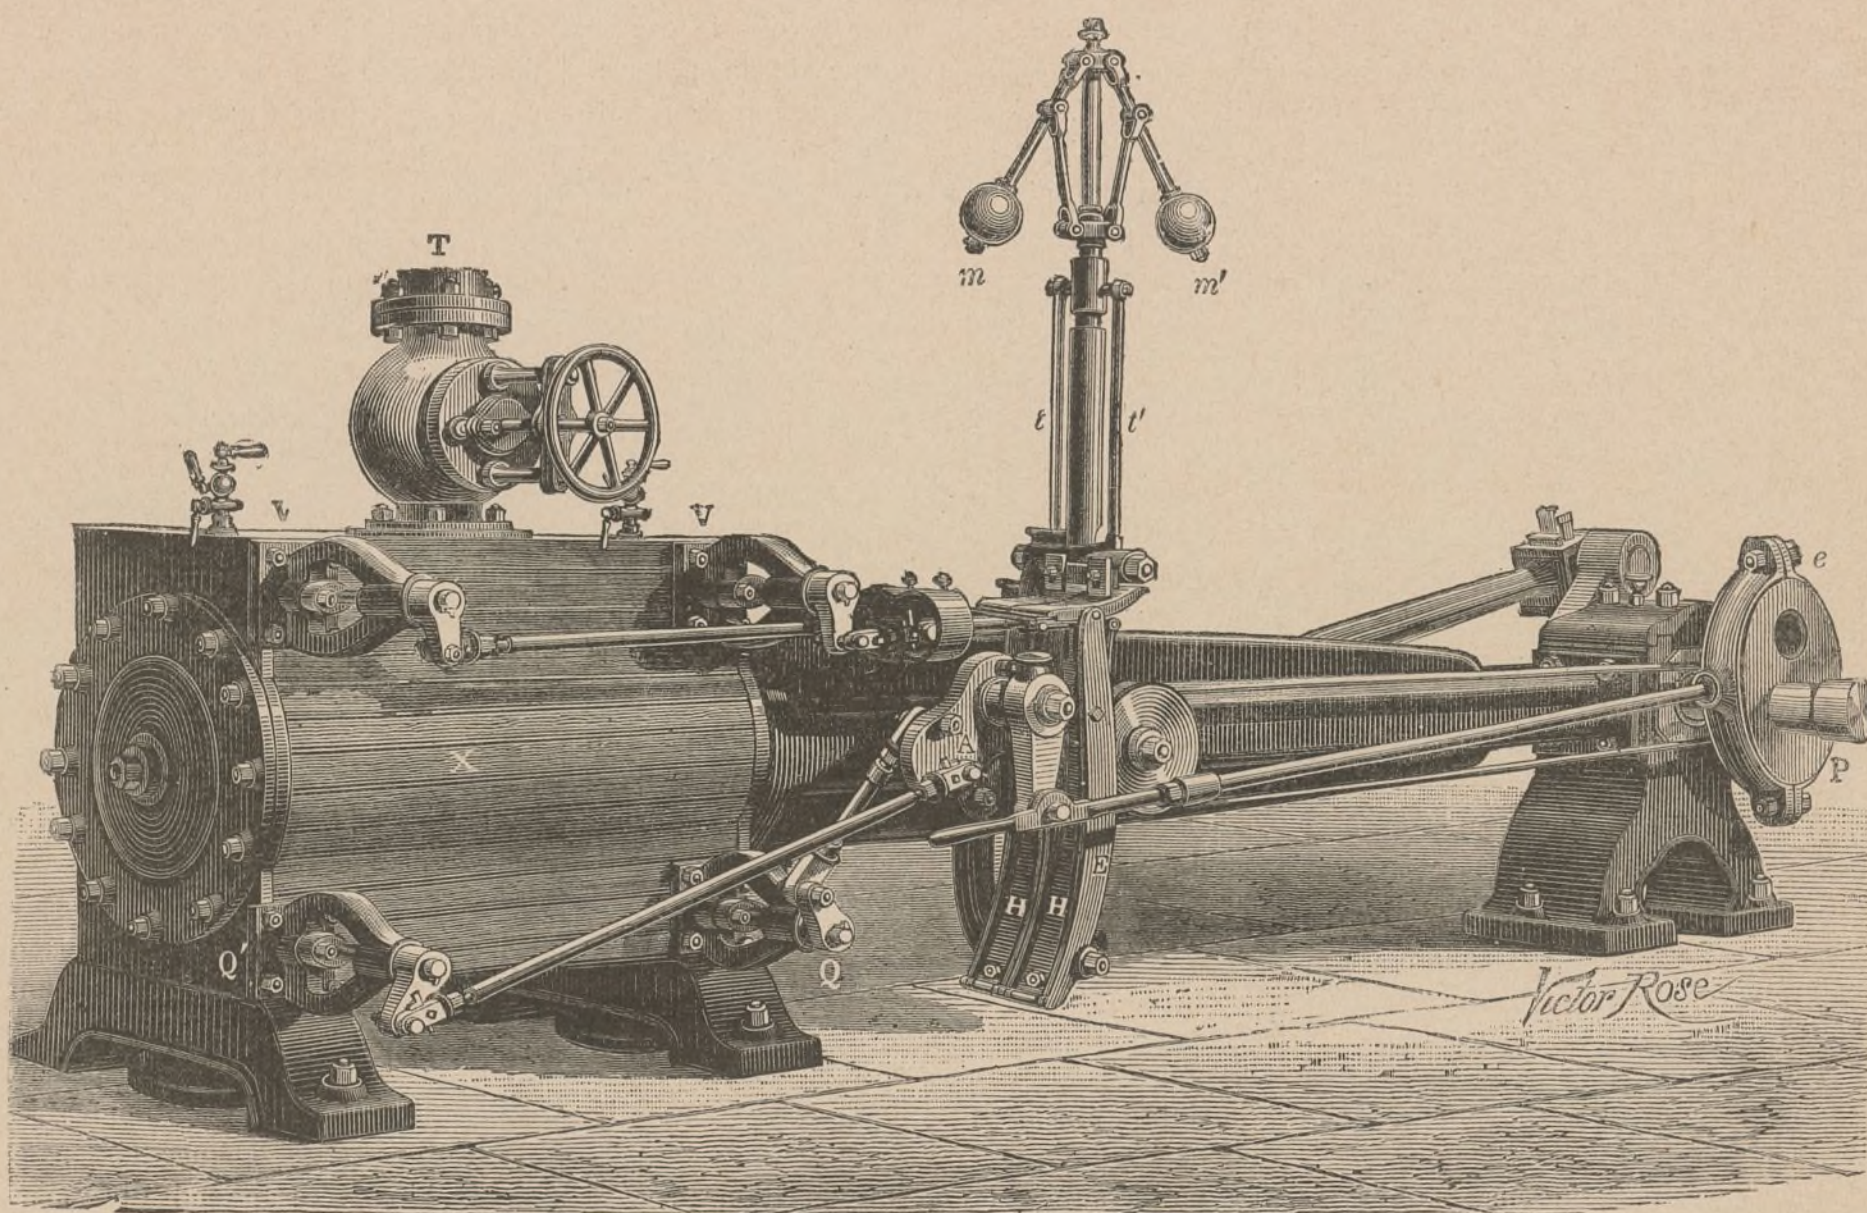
VUE D'ENSEMBLE D'UNE MACHINE CORLISS (TYPE DE 1867).
